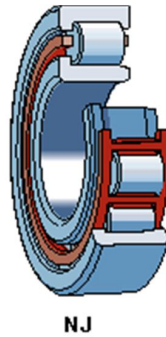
43.- Rodamiento de rodillos cilíndricos, tipo NJ.
